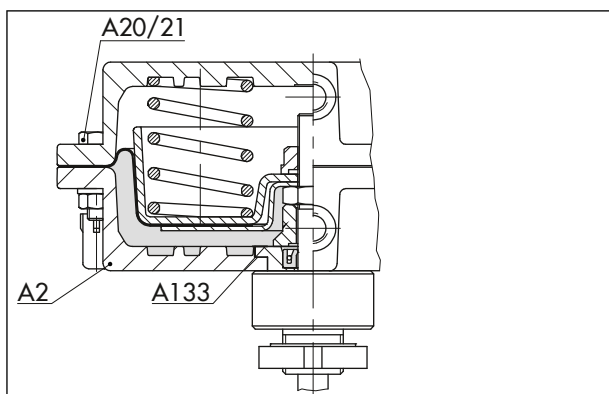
Привод Тип 3271-5 с рабочим направлением FA
